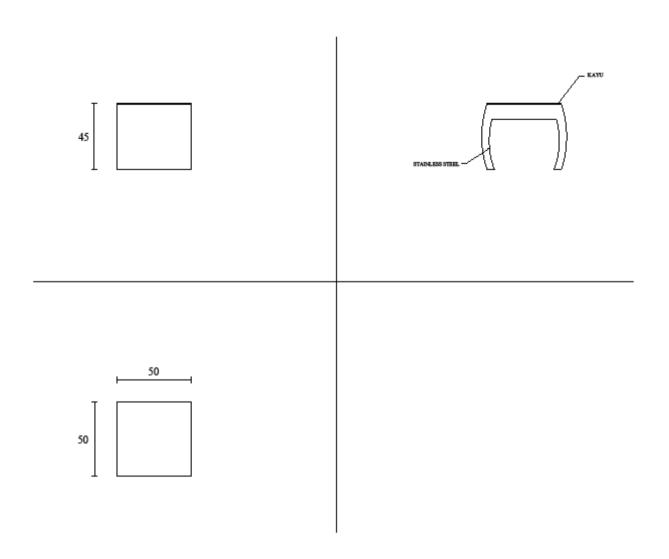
Detail Furnitur 3 (Sundeck 1)
